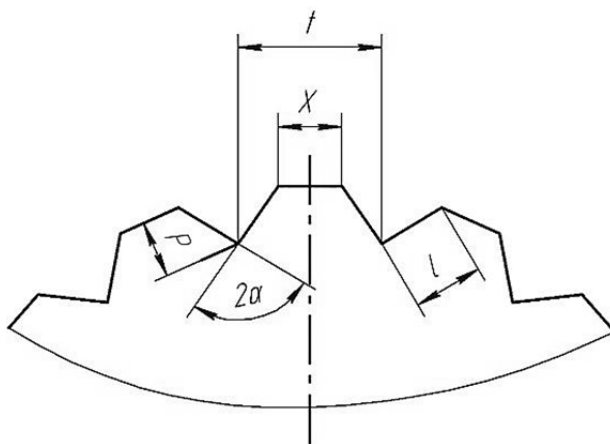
Профиль рифлений на боковой поверхности рабочей части пробивного пуансона
